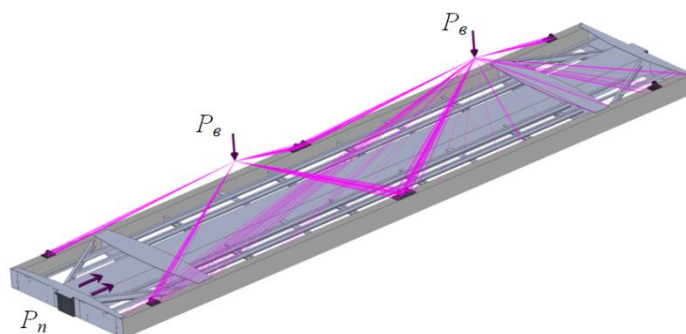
Розрахункова схема несучої конструкції вагона-платформи
